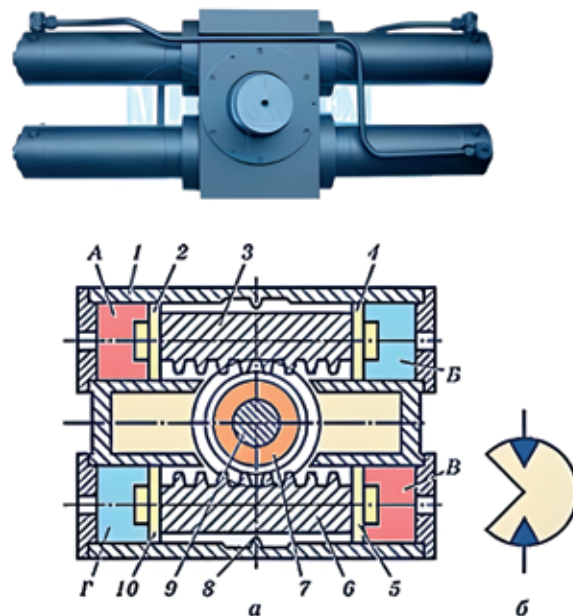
Схема чотирпоршневого дворейкового поворотного гідродвигуна:
